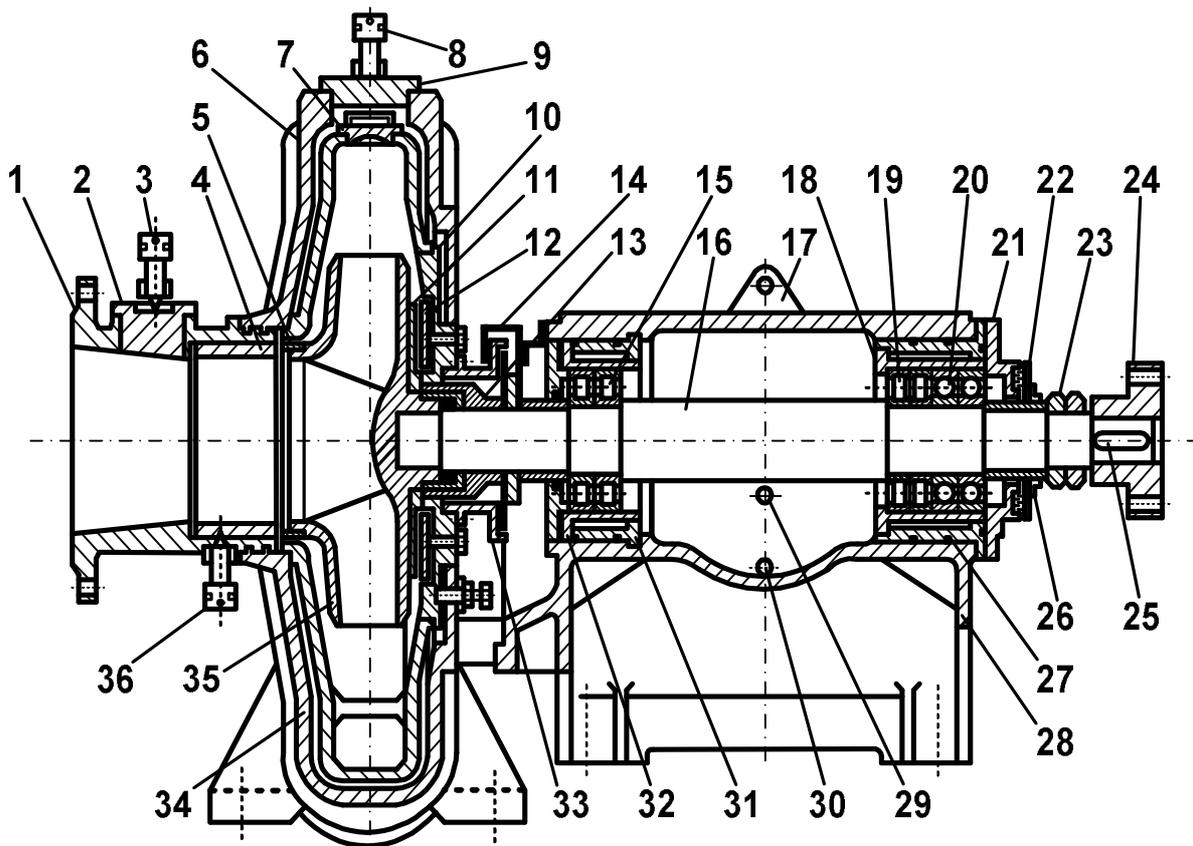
Конструкция углесоса 14У-7: 1 – всасывающий патрубок; 2, 7 и 9 – заглушки патрубка, протектора и корпуса; 3, 8 и 36 – клапаны продувки; 4 – защитная втулка; 5 – уплотнительная втулка; 6 – корпус; 10 – фланец внутренний; 11 и 12 – бронедиски; 13 – дистанционная втулка; 14 – торцевое уплотнение; 15 и 19 – радиальные подшипники; 16 – вал; 17 – рымбол; 18 и 31 – стакан; 20 – радиально-упорные подшипники; 21 – фланец подшипниковой опоры; 22 – лабиринтное уплотнение; 23 – стопорная гайка; 24 – полумуфта; 25 – шпонка; 26 – упорная втулка; 27 – кольцевое уплотнение; 28 – станина; 29 – смотровое стекло; 30 – сливная пробка; 32 – гильза; 33 – фланец ограждения; 34 – протектор; 35 – колесо
